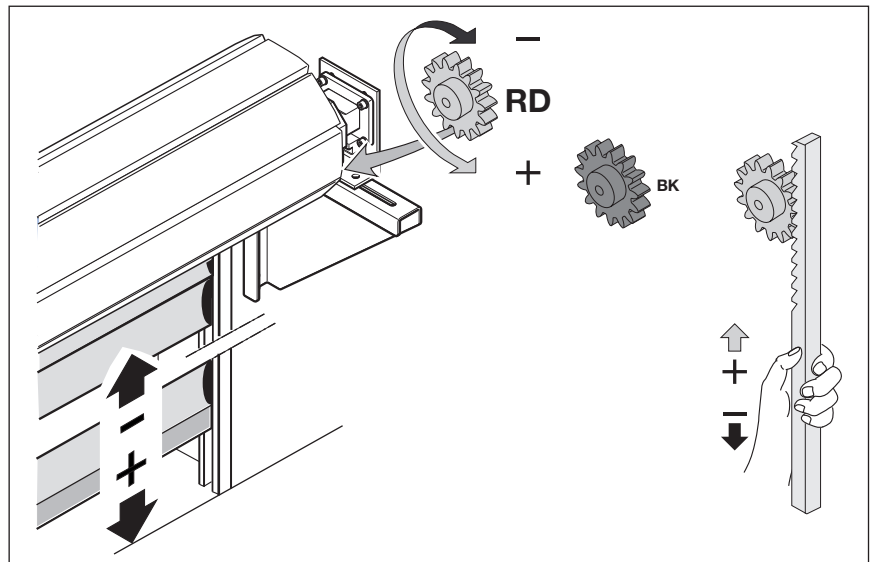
Винт с рифленной головкой RD для конечного положения *Ворота Закр.*, приспособление для регулировки
